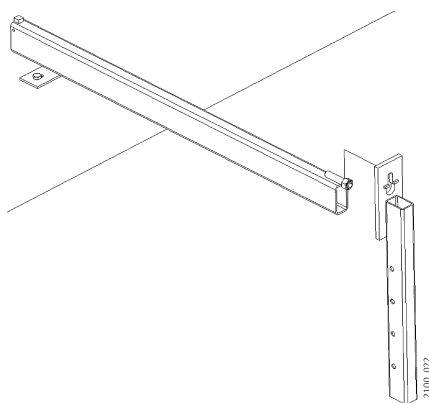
Montage der Schraubbefestigung am Hängeplattformträger
